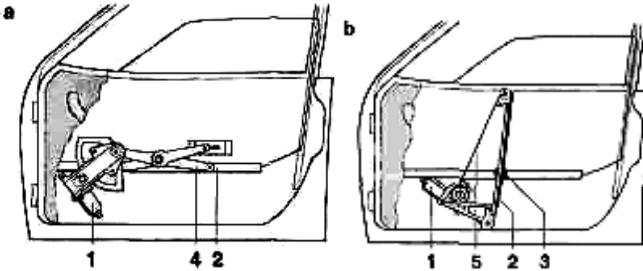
Приводи склопідйомників: а - система з регулятором; б - система з гнучким тросом Боудена: 1 - електричний двигун із зубчатим редуктором; 2 - направляюча обойма; 3 - контрольний стрижень; 4 - підйомний механізм; 5 - гнучкий приводний трос
